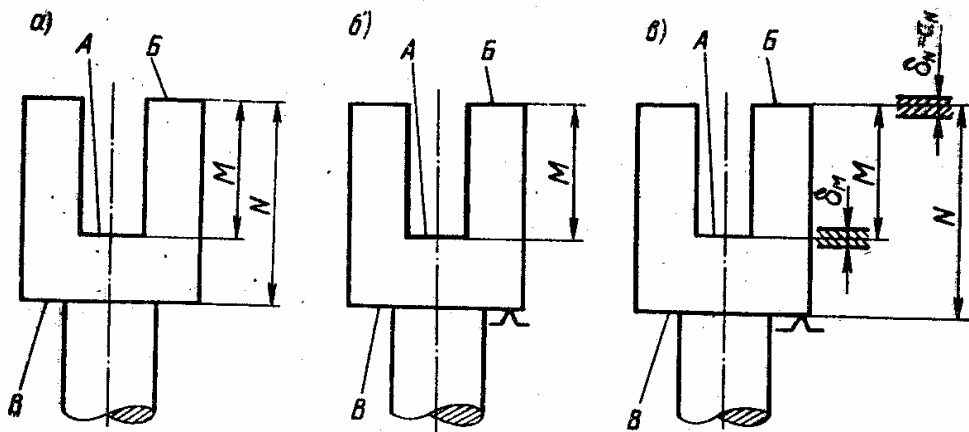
Обработка детали при несовмещении установочной базы с исходной:
